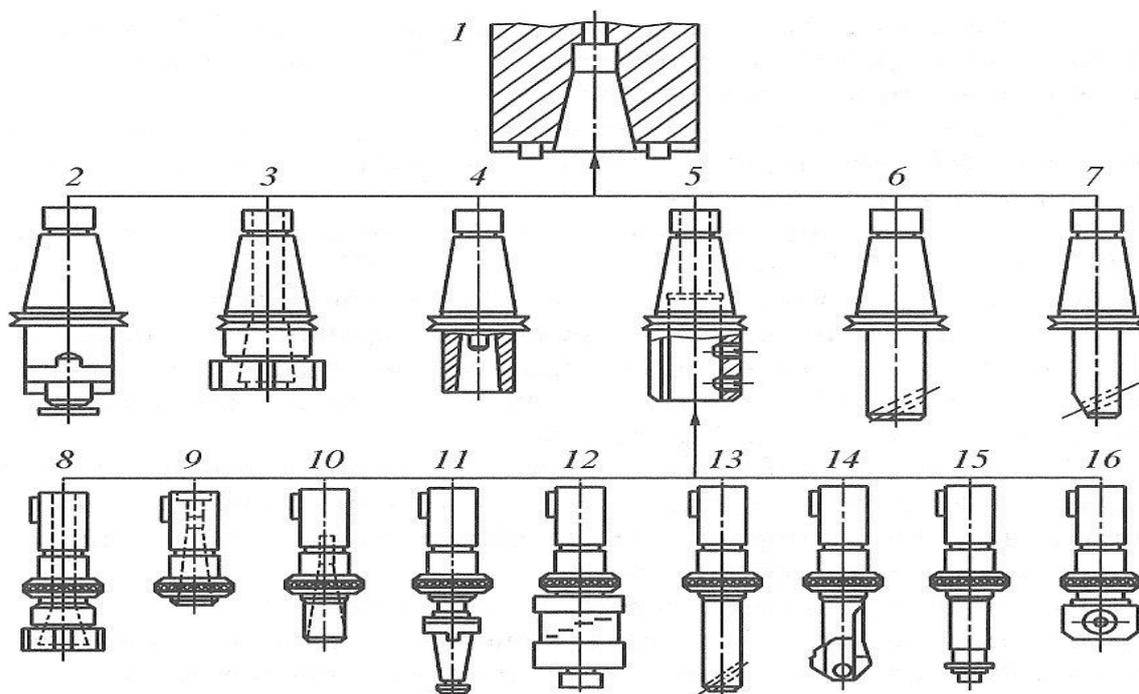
Система вспомогательного инструмента для сверлильно-фрезерно-расточных ГПМ:
